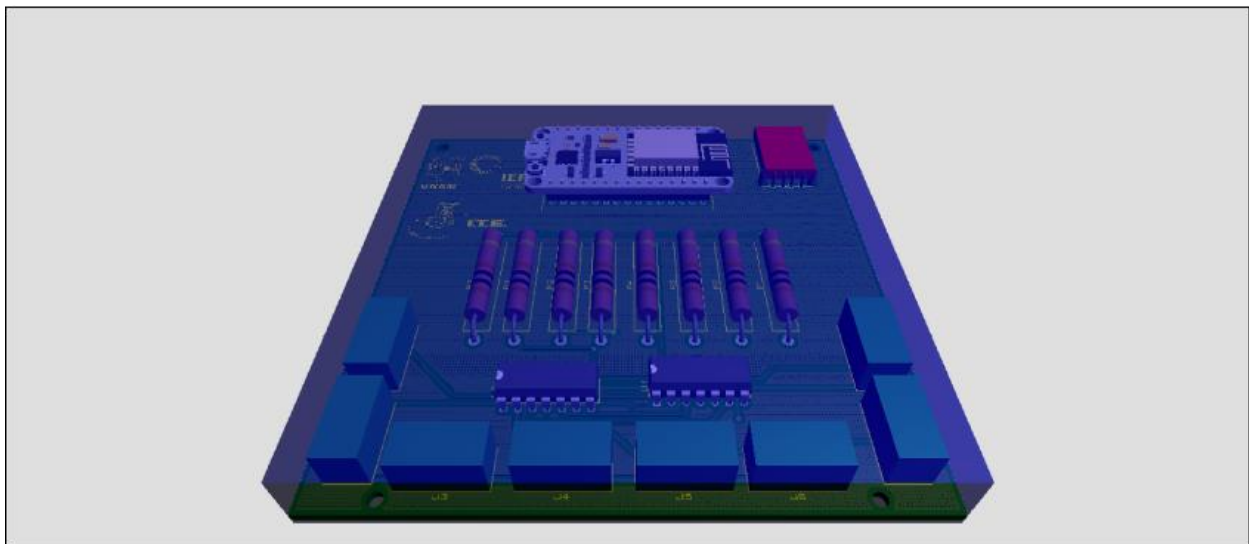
Presentación 3D con altura del diseño PCB en el software de Proteus
